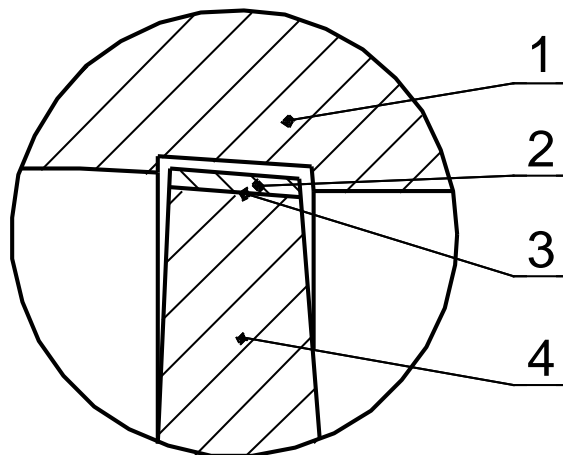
Пара тертя «торець лопатки–корпус ГТД»:
